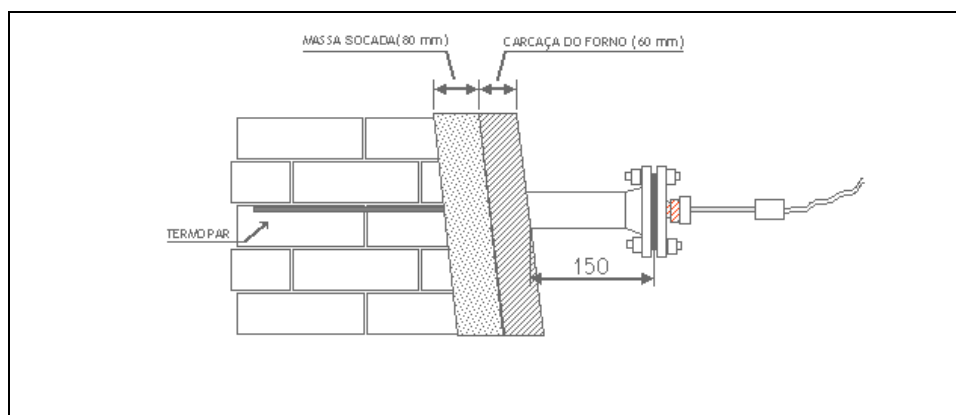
Configuração da instalação dos termopares e as medidas das carcaça metálica e a massa socada
